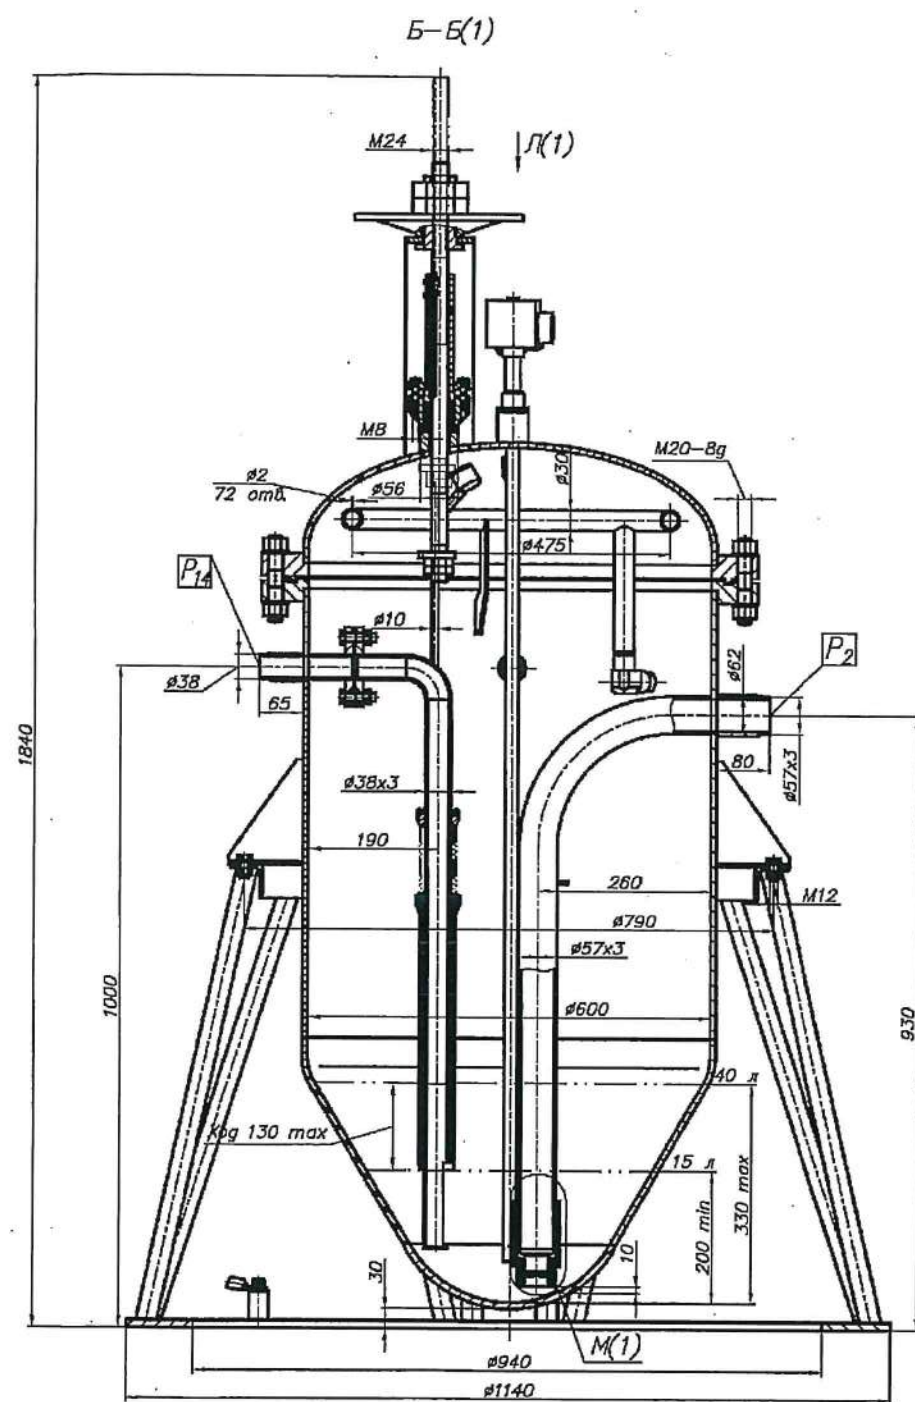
Габаритные, присоединительные размеры и конструктивное устройство мерника
